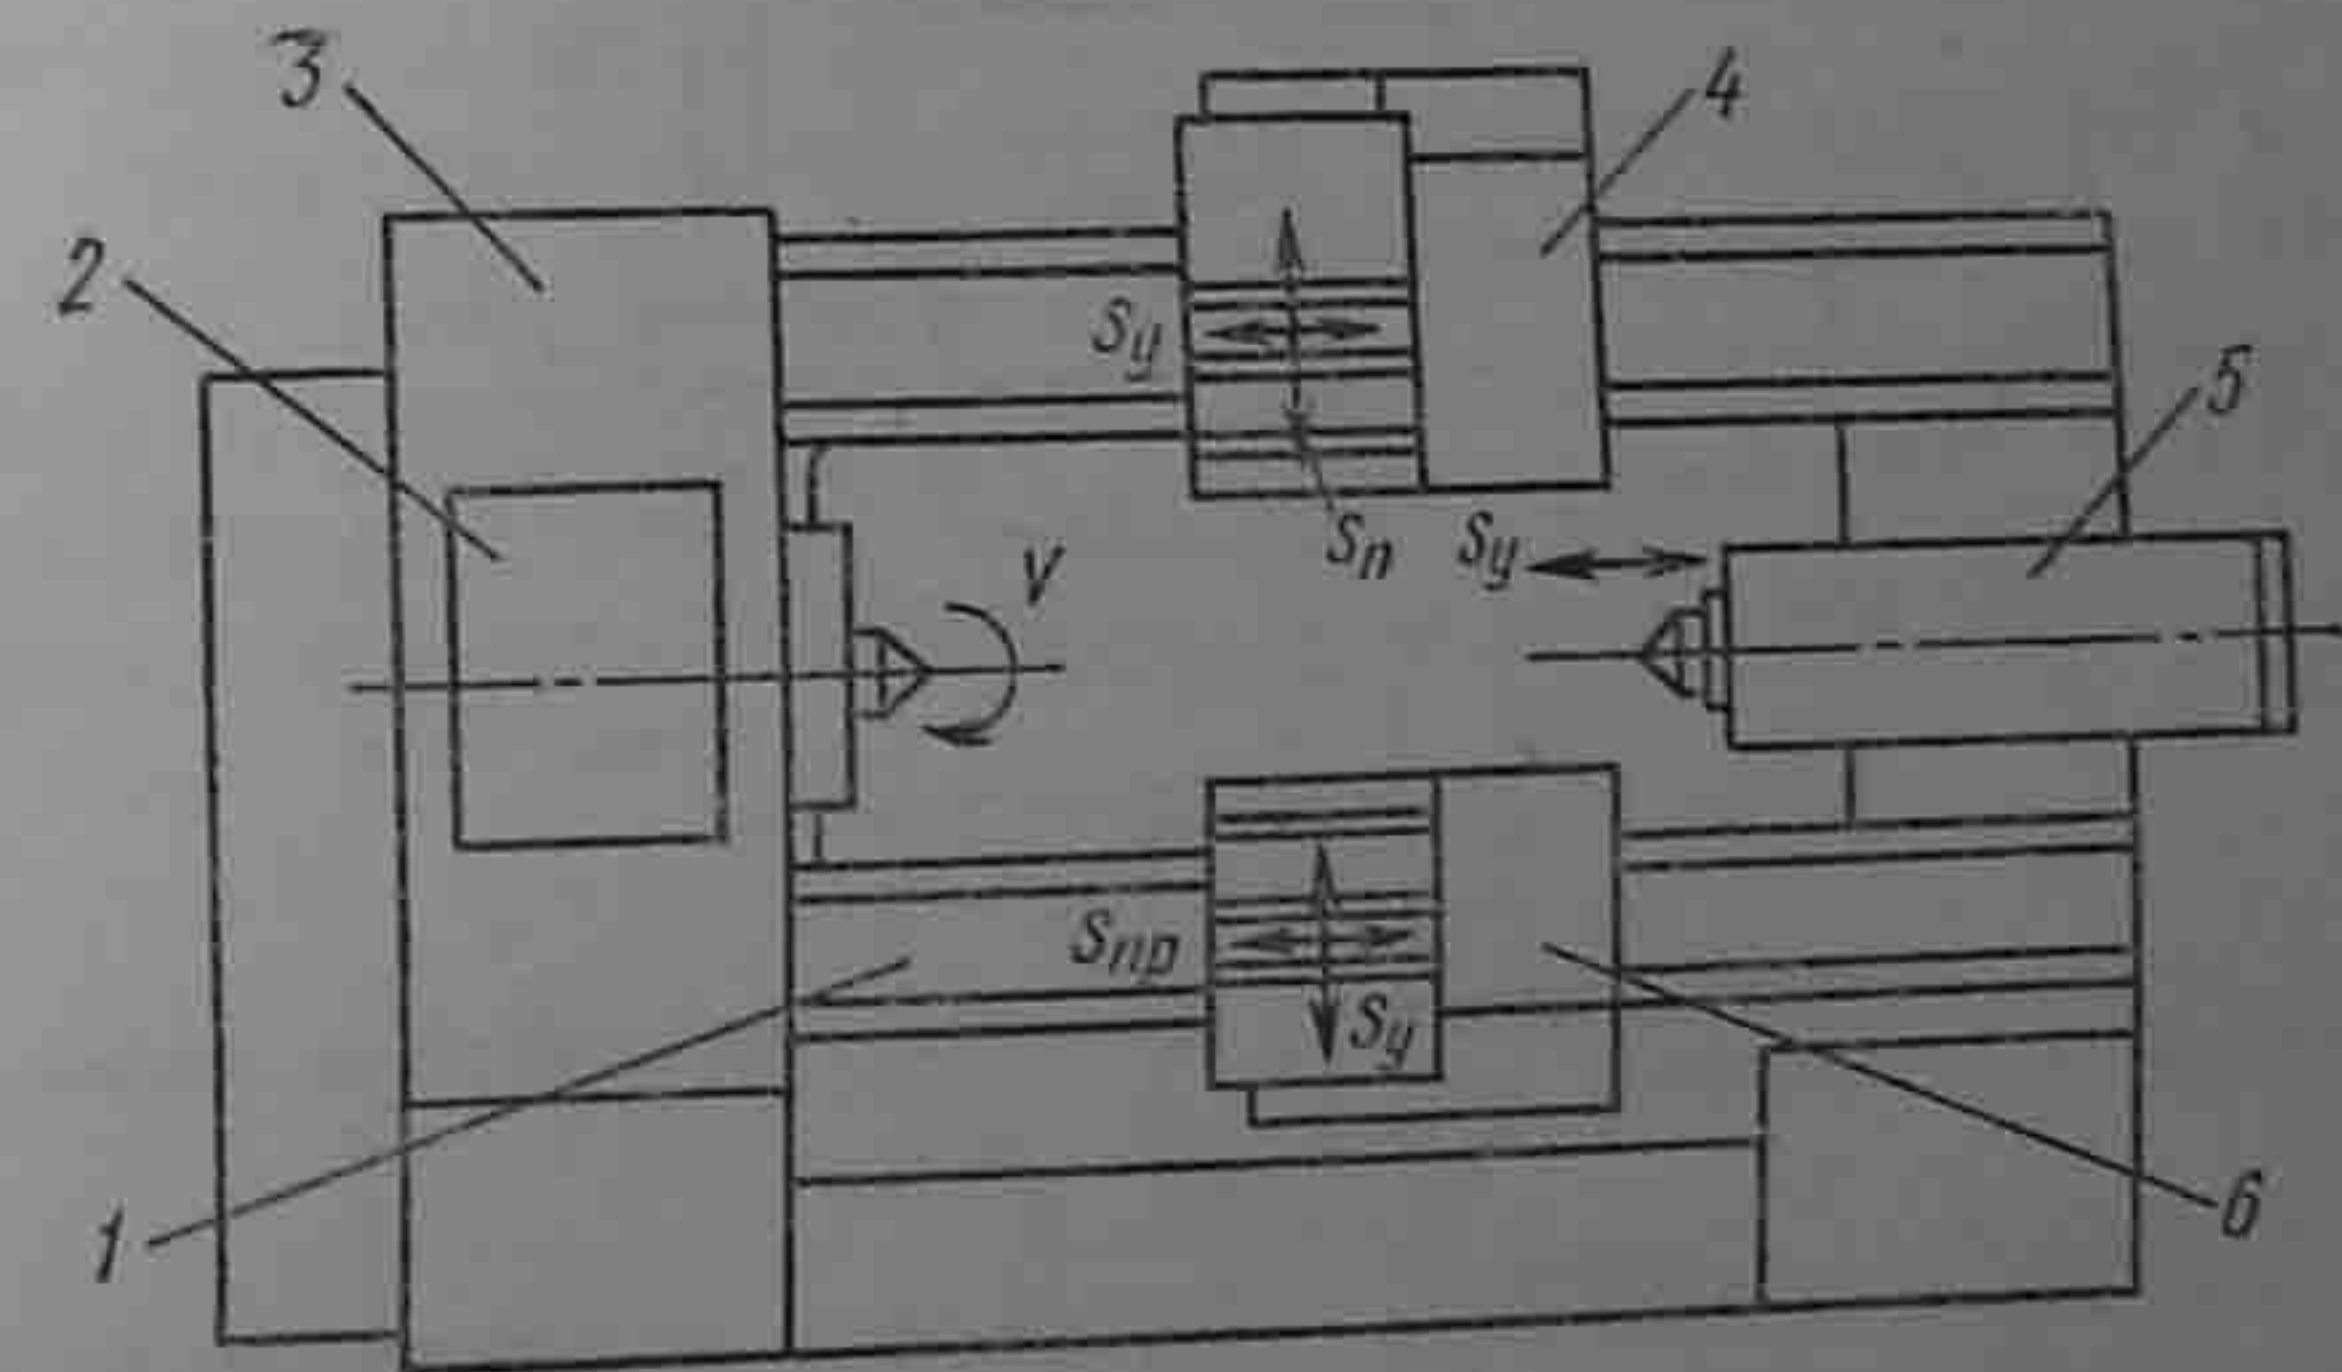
Общий вид токарного многолезцового полуавтомата
